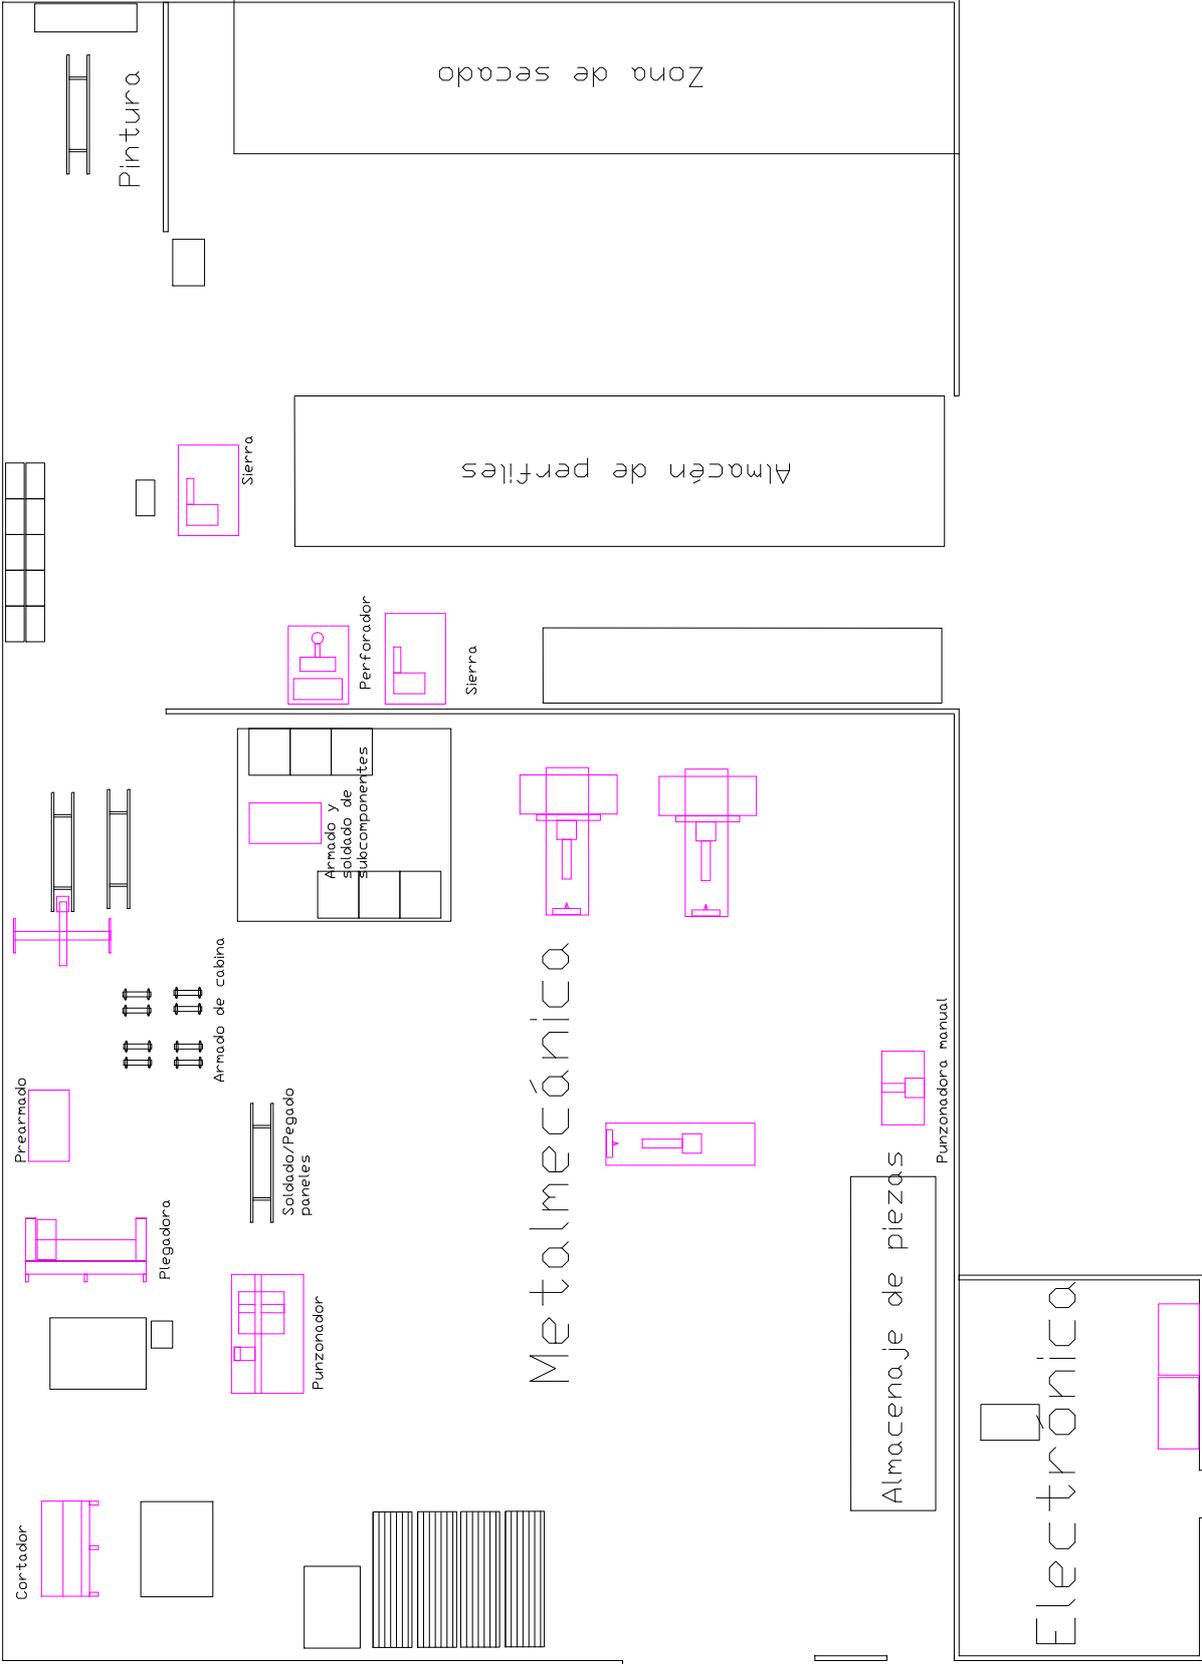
Layout de planta de fabricación. Fuente: elaboración propia
